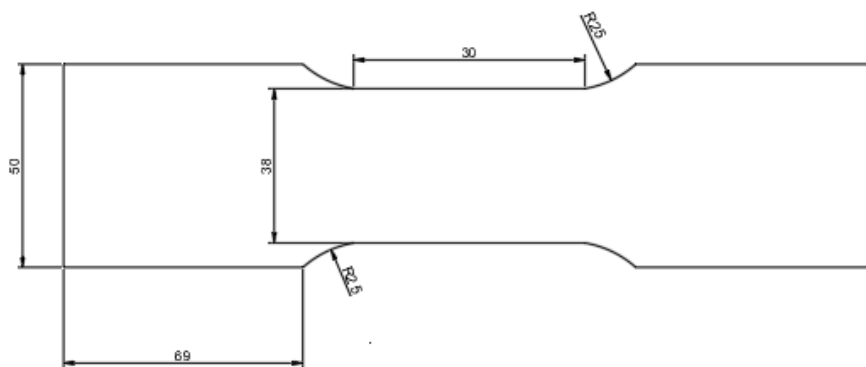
Exemple d'éprouvette de traction (dimension en mm)
